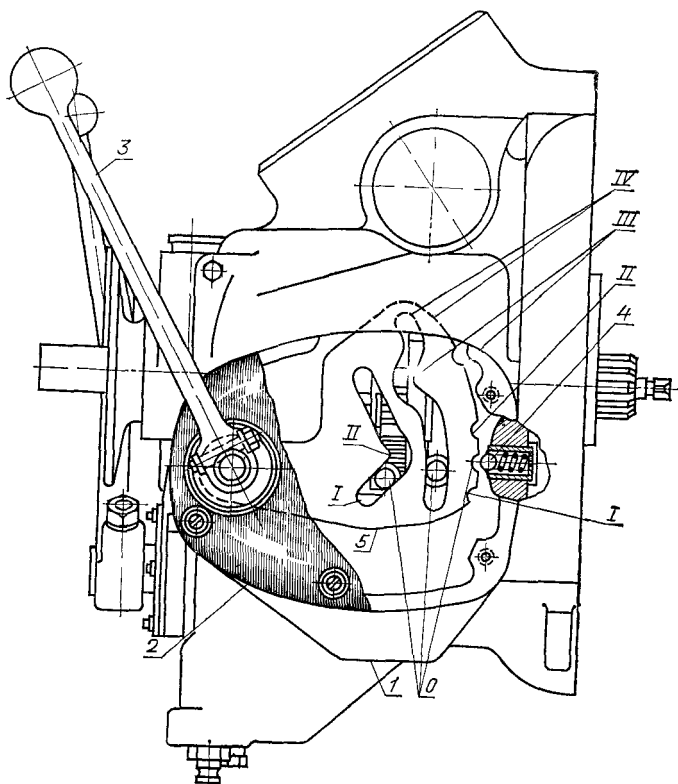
Установка специальной крышки с гисезом для наблюдения за полнотой включения передач:
